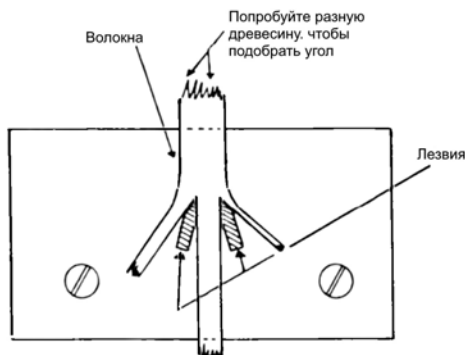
Устройство для расщепления заготовки под нагели.
